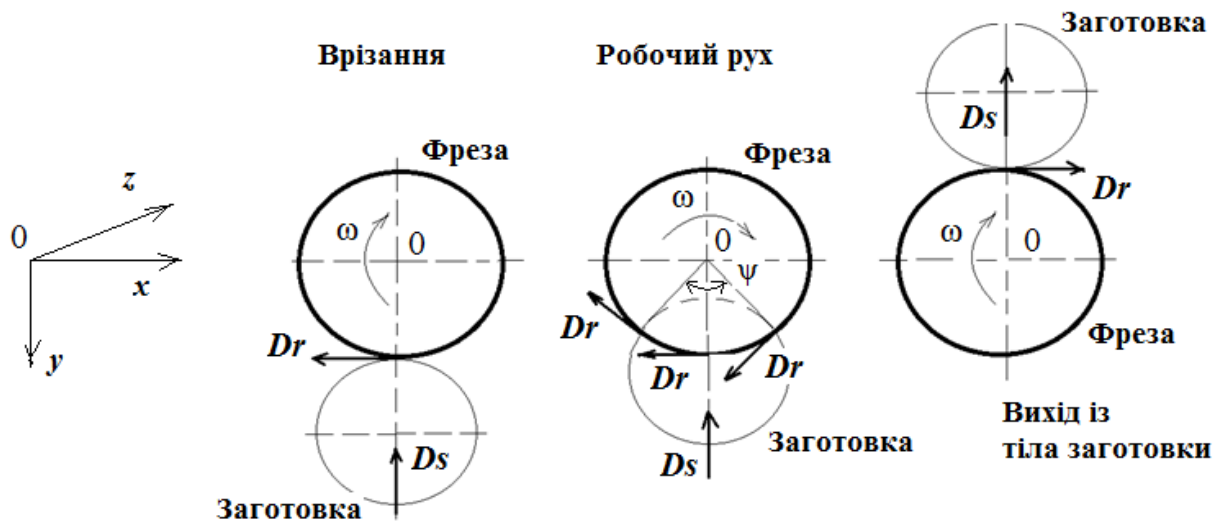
Схеми фрезерування на фрезерно-центрувальному верстаті
